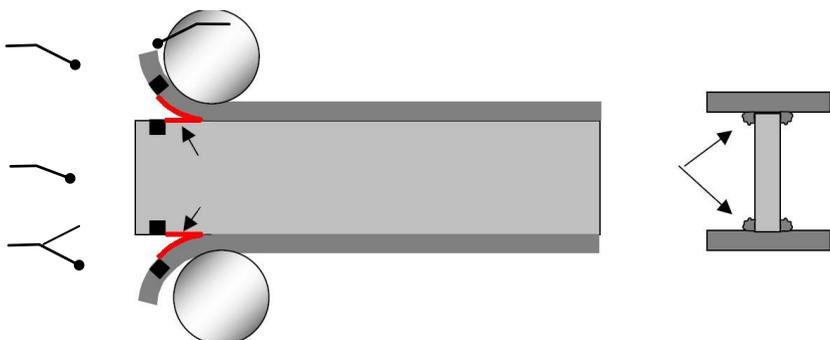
Схема сварки балки с нагревом токами высокой частоты.
